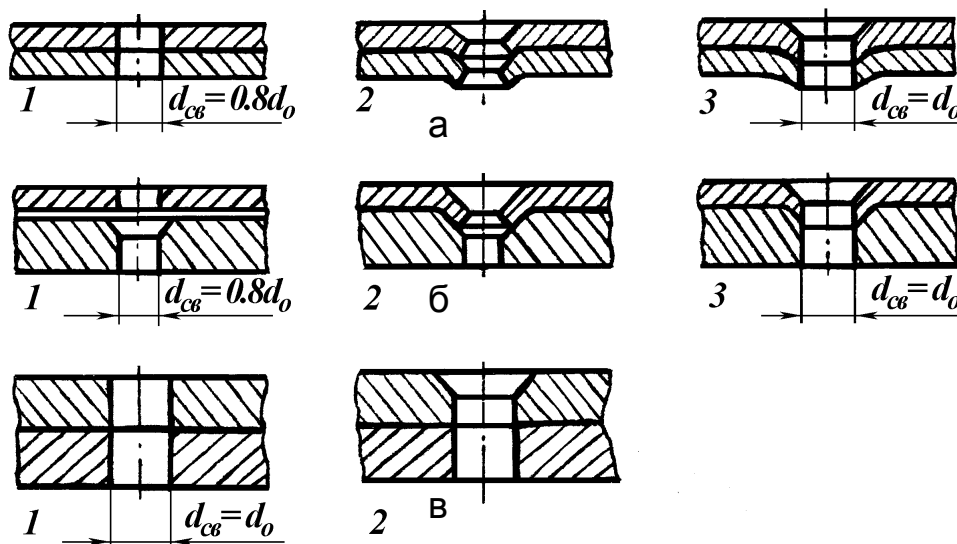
Способы образования гнезд под головки потайных заклёпок: а – штамповка в обеих деталях; б – зенкование в каркасе и штамповка в обшивке; в – зенкование в обшивке (1 – сверление отверстий; 2 – зенкование гнезда; 3 – рассверливание отверстий)
